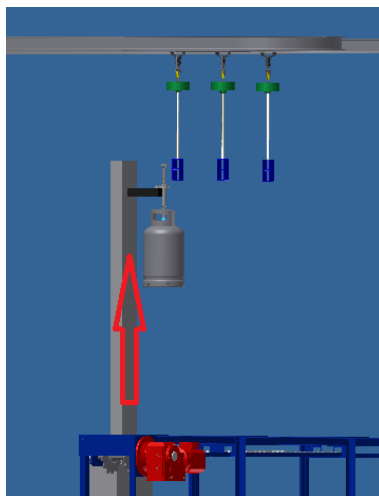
Elevação da garrafa até ao ponto de acoplamento
